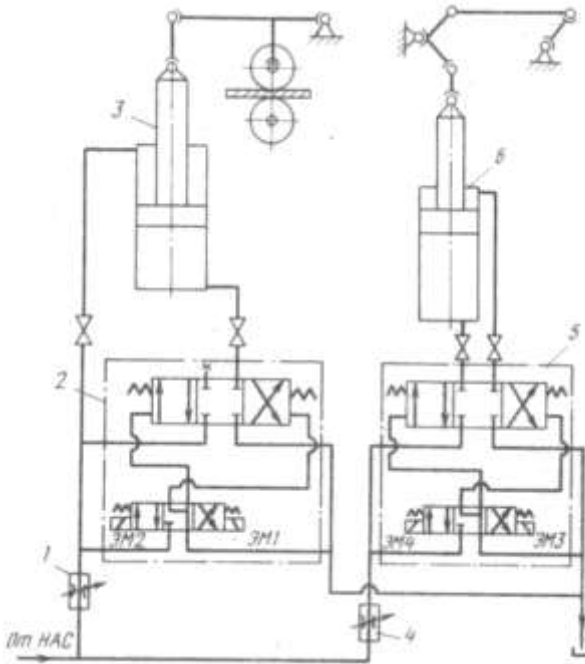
Гидросхема привода верхнего ролика тянуще-правильной машины и поворотного лотка машин непрерывного литья заготовок
